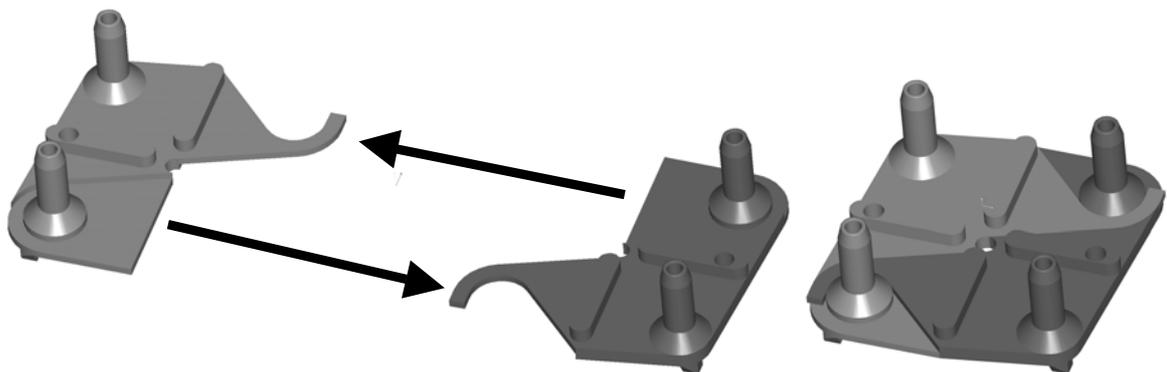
Modulverbinder, einzelne Zweierstecker (links) und montiert zum Viererstecker (rechts)
